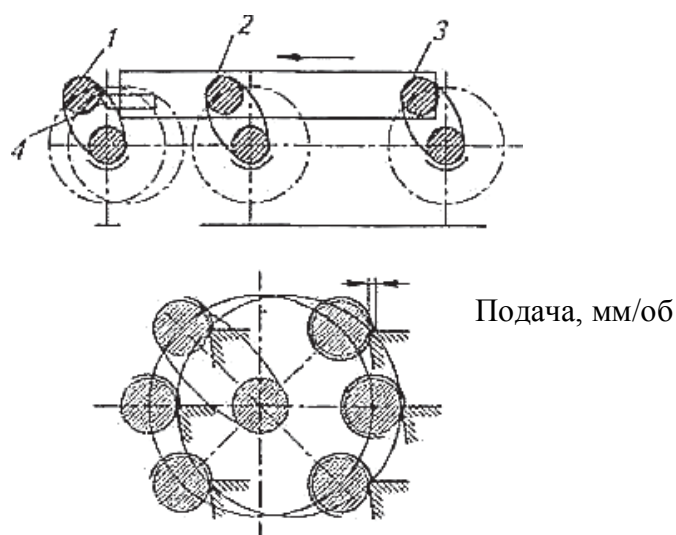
Схема работы станка для одновременного точения всех шатунных шеек коленчатого вала: 1 – обрабатываемый вал; 2, 3 – копирные коленчатые валы; 4 – резец
